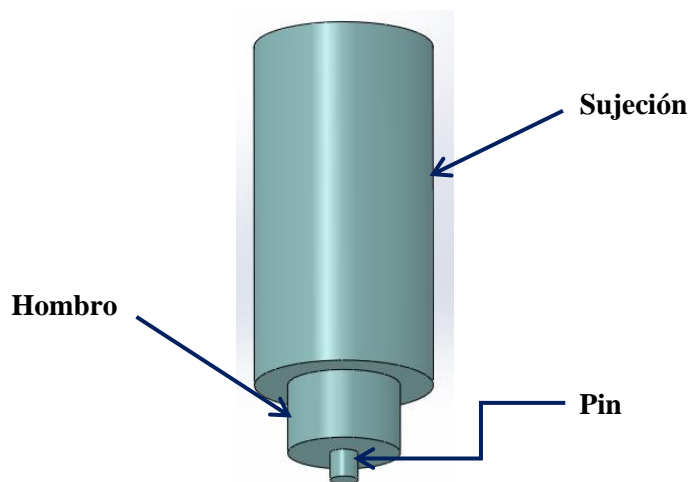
Esquema de la herramienta de soldadura con pin cilíndrico
